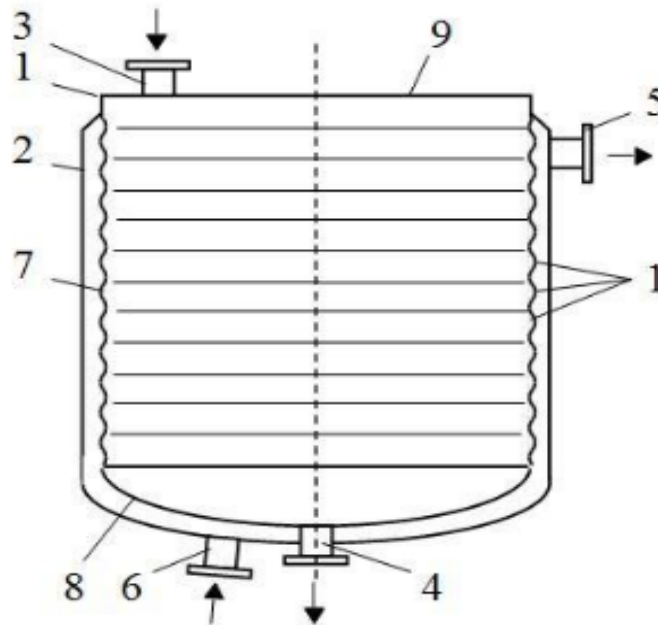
Конструкція змішувача для пластичних мас [складено автором на основі джерела 17]: 1 – корпус змішувача; 2 – мембранна оболонка; 3 – вхідний патрубок для інжекції колоїдного розчину; 4 – патрубок для виходу гомогенної суміші; 5, 6 – патрубки для прокачування теплоносія; 7 – обичайка; 8 – днище змішувача; 9 – кришка змішувача
